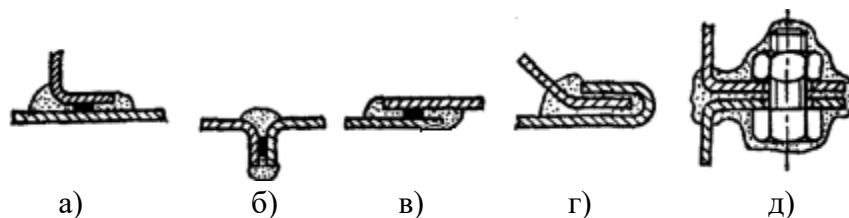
Основные соединения кузовных деталей в которых образуются щели: а, б, в – виды точечной сварки; г – фальцевое соединение; д – болтовое соединение.
